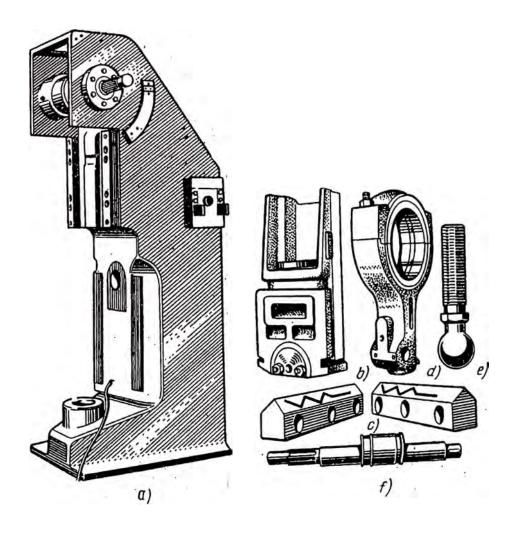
Unidades (conjuntos) de montaje principales de la prensa mecánica:
